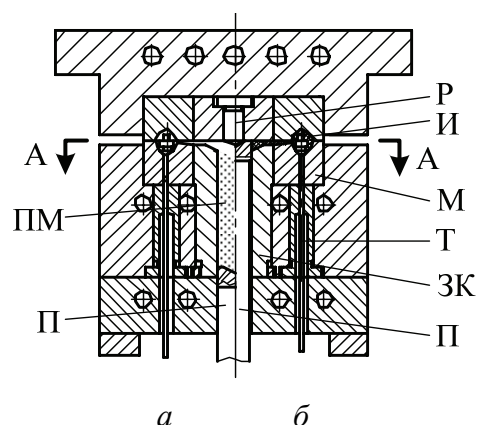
Пресс-форма с нижней загрузочной камерой до начала прессования (а) и после оформления изделия (б): П – пуансон; ПМ – пресс-масса; Р – рассекатель; И – изделие; М – матрица; Т – толкатель; ЗК – загрузочная камера
